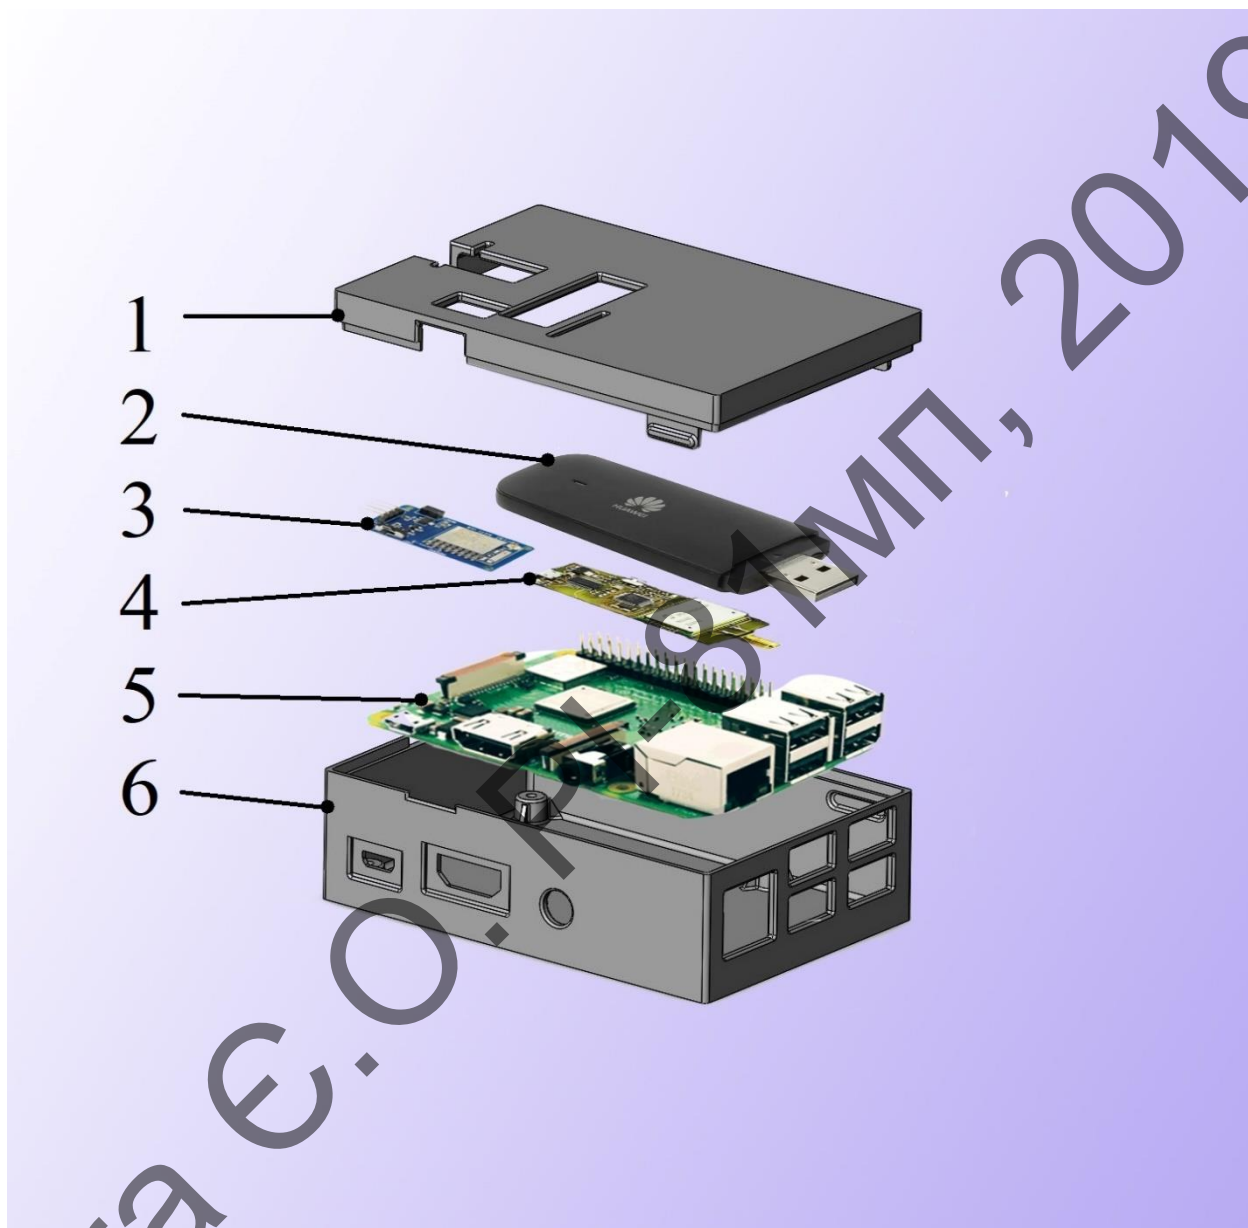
Схема розміщення елементів, де 1 – кришка корпусу;
